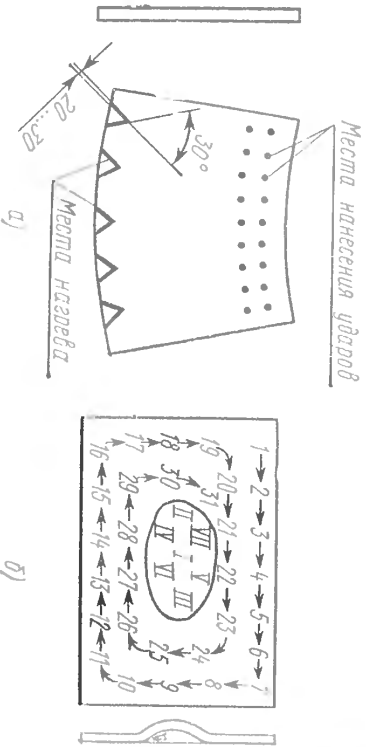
Схемы правки плоской заготовки с серповидным прогибом (а) и выпучиной (б): 1...31 — места нанесения ударов; I...VII — зоны нагрева
